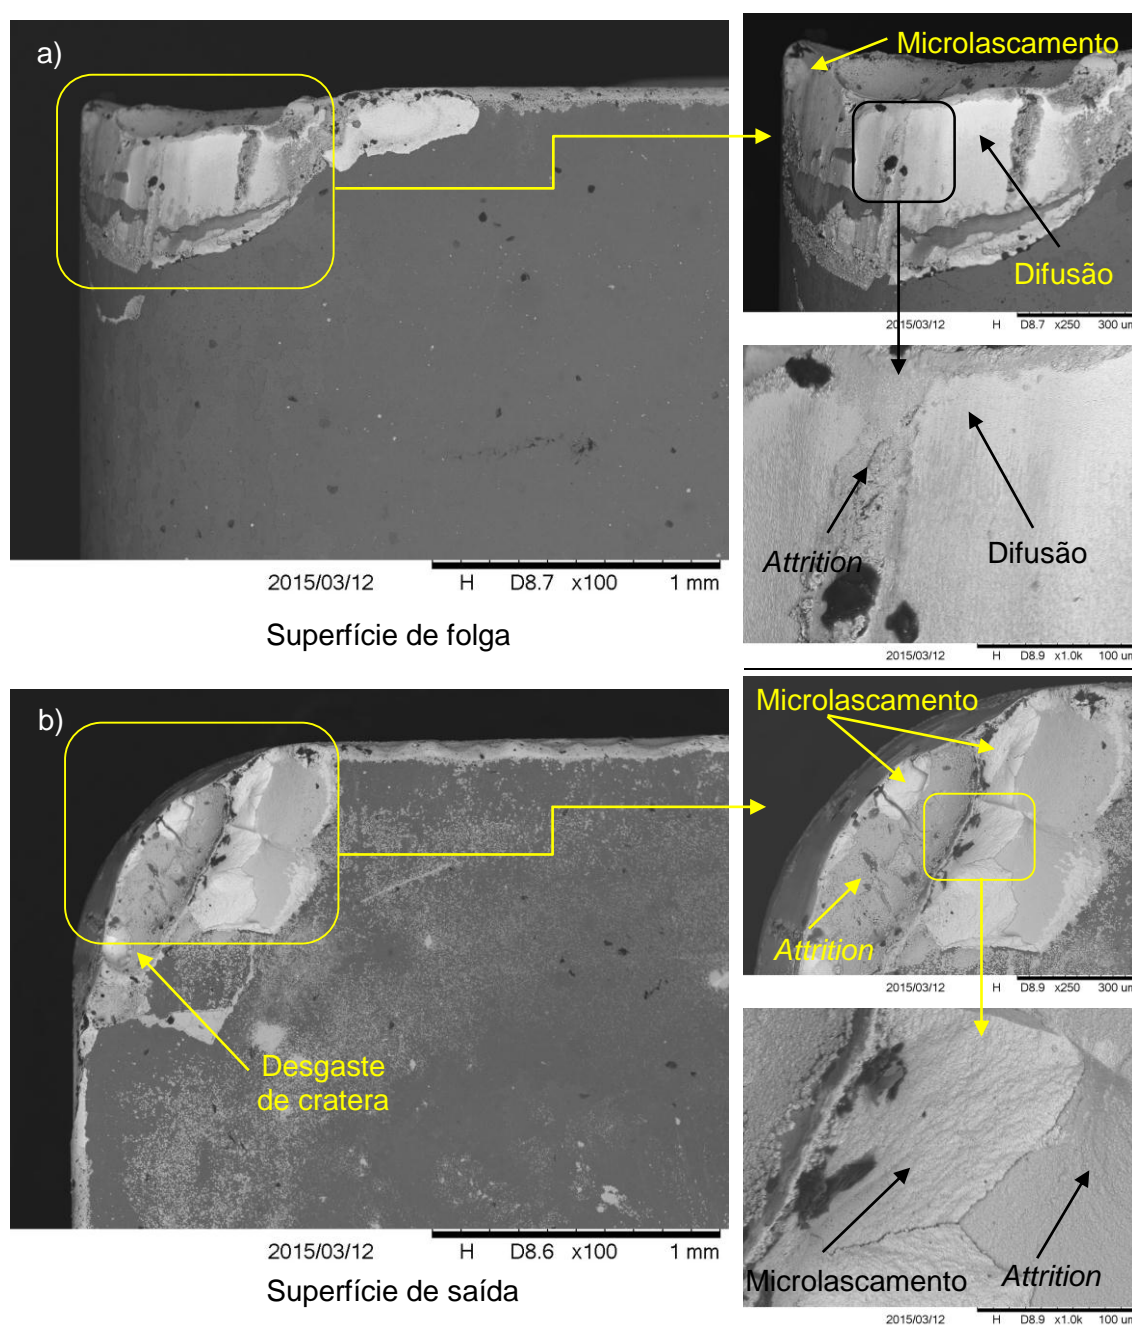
Fotos obtidas através do MEV das ferramentas de metal duro após a usinagem do Inconel 718 com aplicação de fluido de corte Vasco 1000 + 5% de MoS_2 por jorro. (a) superfície de folga e (b) superfície de saída. Velocidade de corte 50 m/min, avanço 0,1 mm/rot e profundidade de corte de 0,5 mm.
